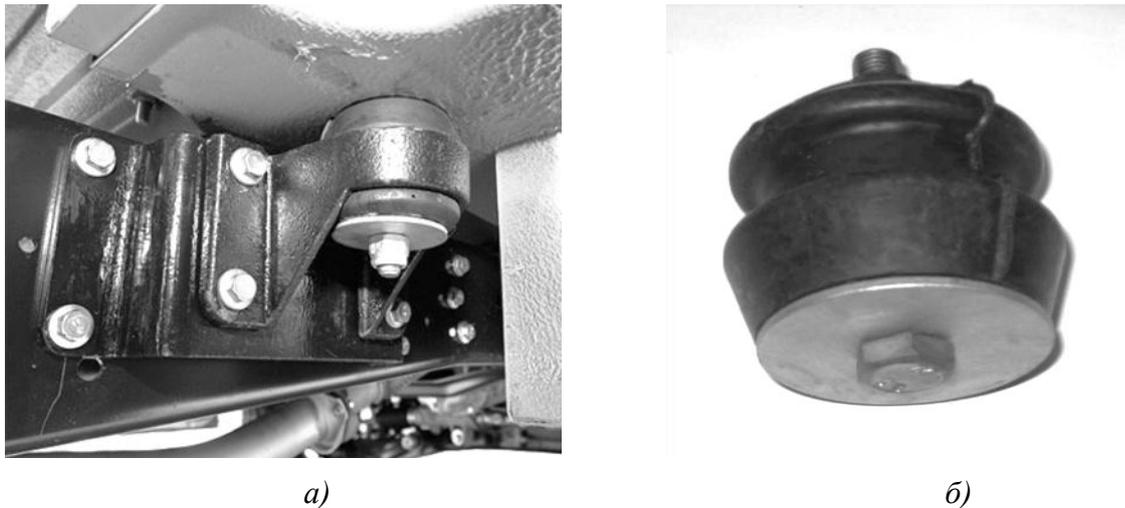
Резино-металлический элемент крепления кабины к раме:
